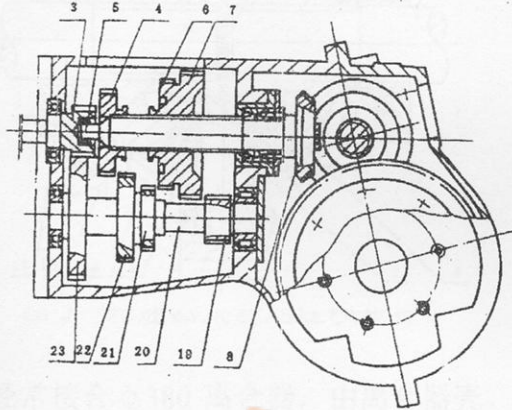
所示为换向机构，位于变速箱中部，在传动轴后端固定有小伞齿轮 8 与两个大伞齿轮啮合。两个大伞齿轮在换向轴 3 上作相反方向的空转，当滑动换向齿轮 16 与任一个大伞齿轮内齿啮合时，使 16 得到不同方向旋转而起到换向作用，齿轮 16 与差速器的大齿轮啮合。
